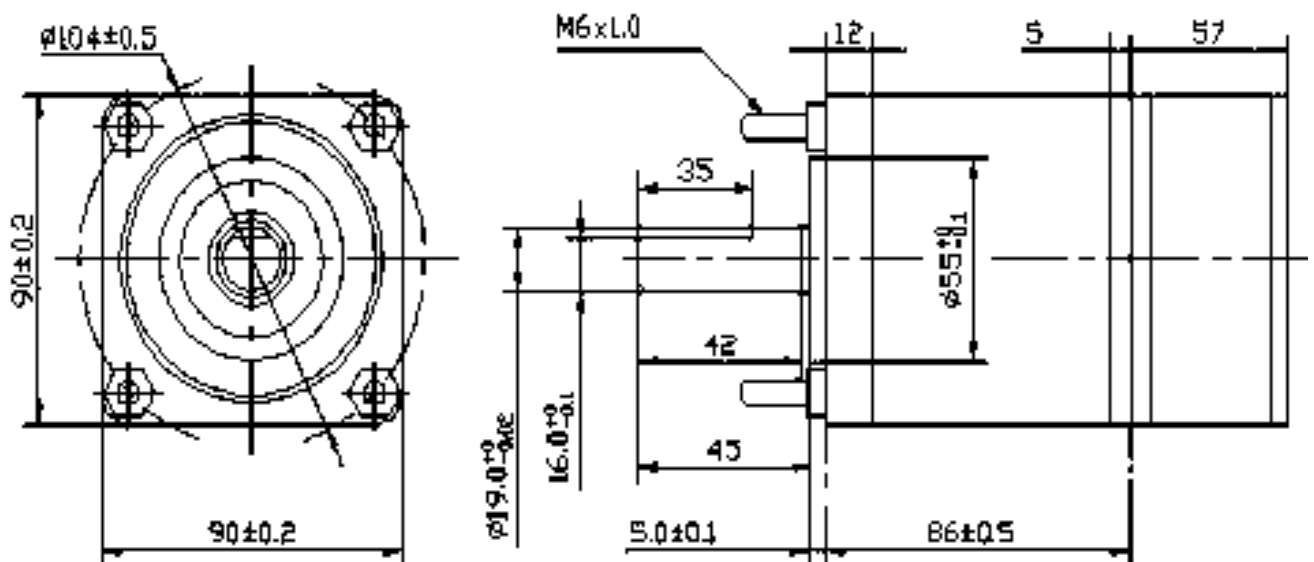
Габаритные и присоединительные размеры планетарного бесколлекторного мотор-редуктора IG-90WGM
